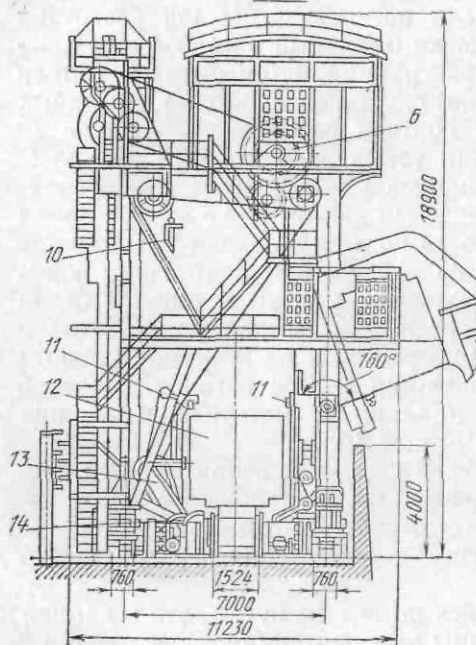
Передвижной башенный вагонопрокидыватель с толкателем
